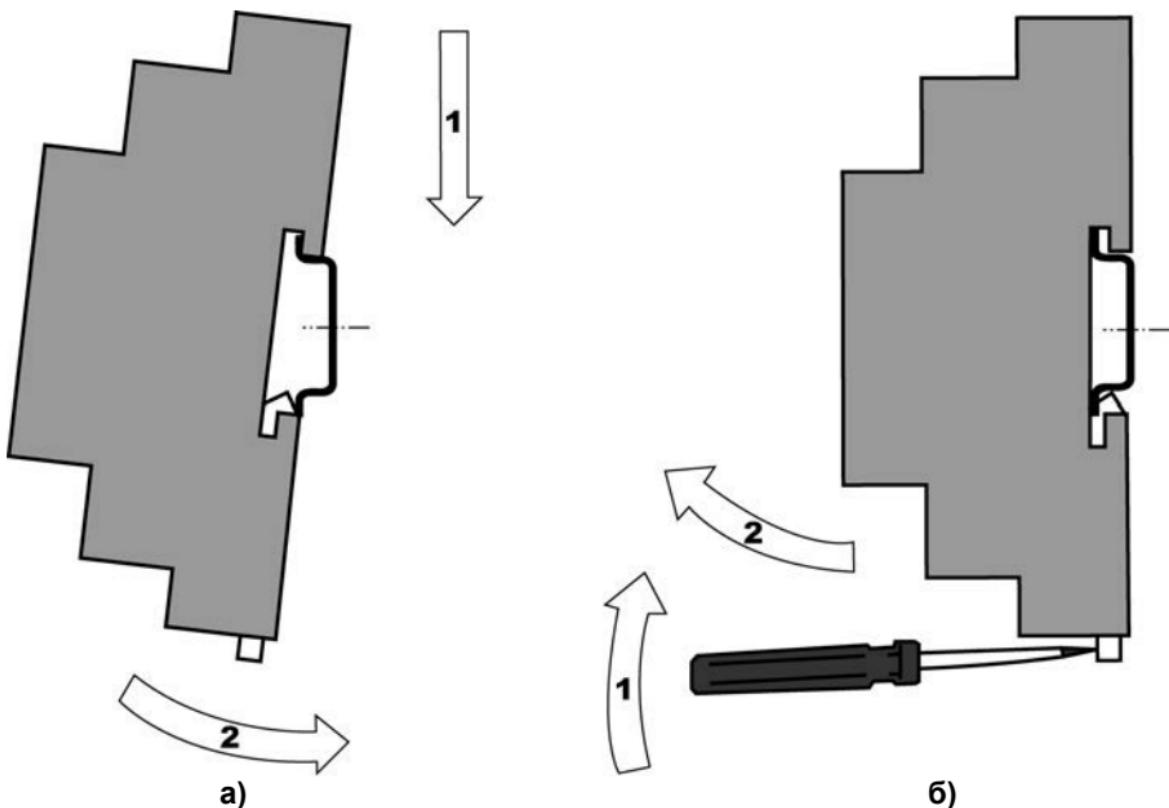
Монтаж контроллера с креплением на DIN-рейку
